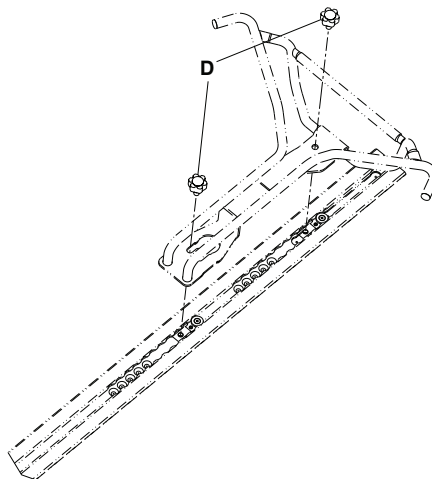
Роговидный фиксатор в сборе с серебристыми ручками (6390-001-033)
